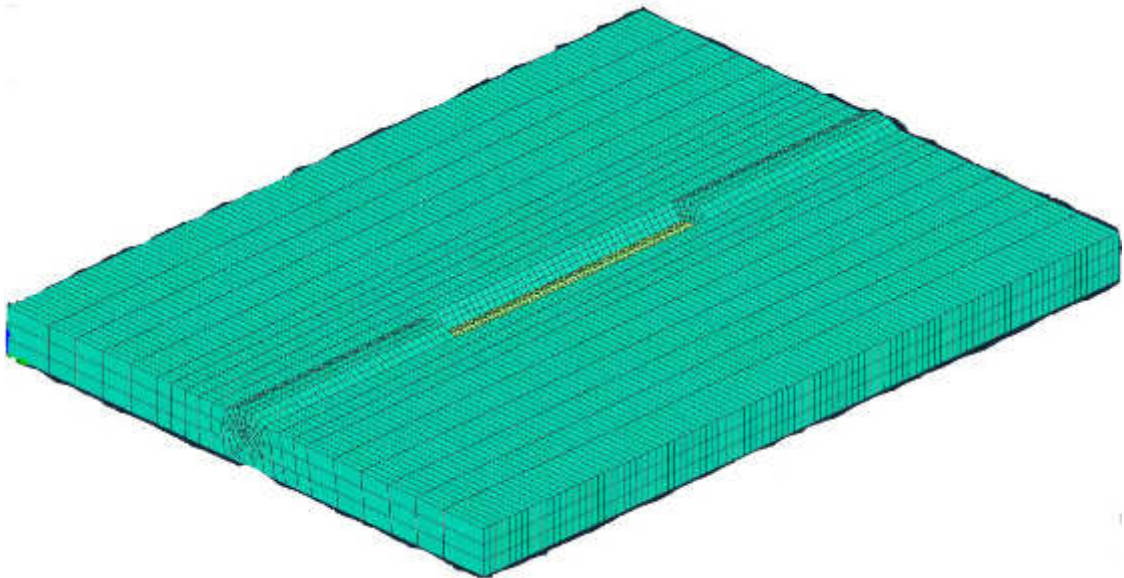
Модель сварочной пробы «Теккен»
